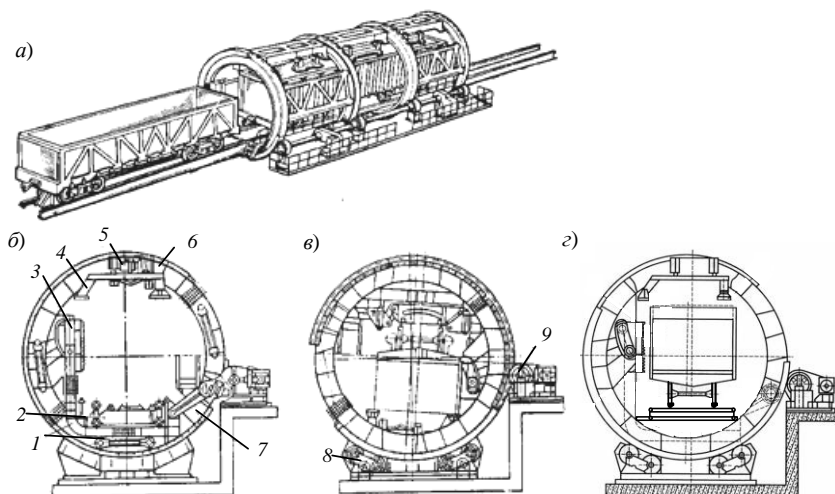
Роторные вагоноопрокидыватели:
